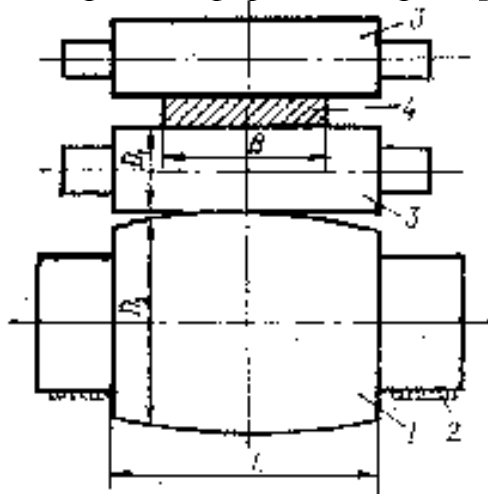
Модель кліті кварто:1 – опорний валок; 2 – опори шийок валка; 3 - рабочие валки; 4 – алюминиевая пластина
